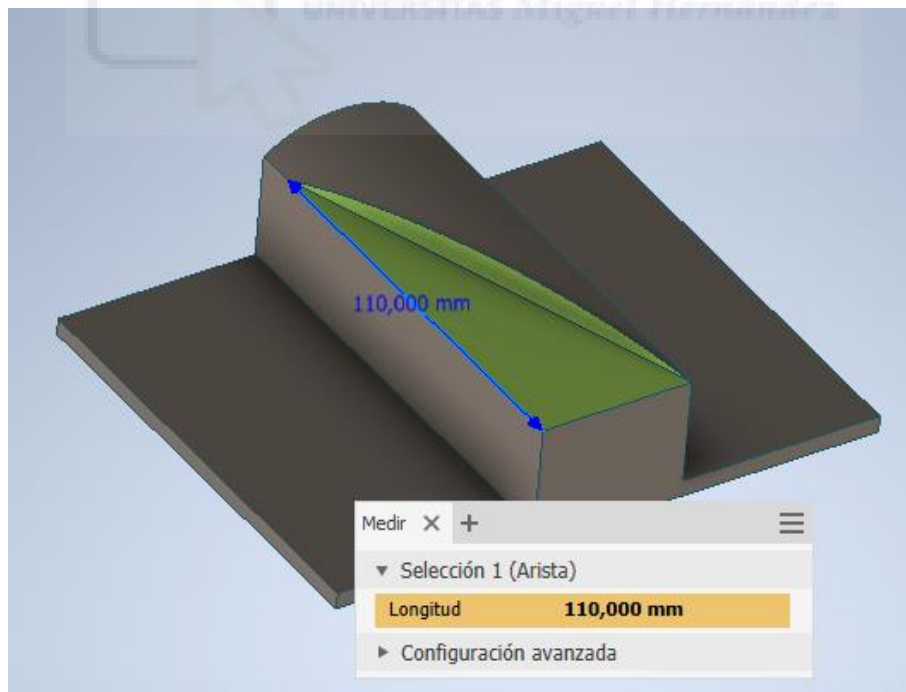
Detalle avance Referencia Soldadura
